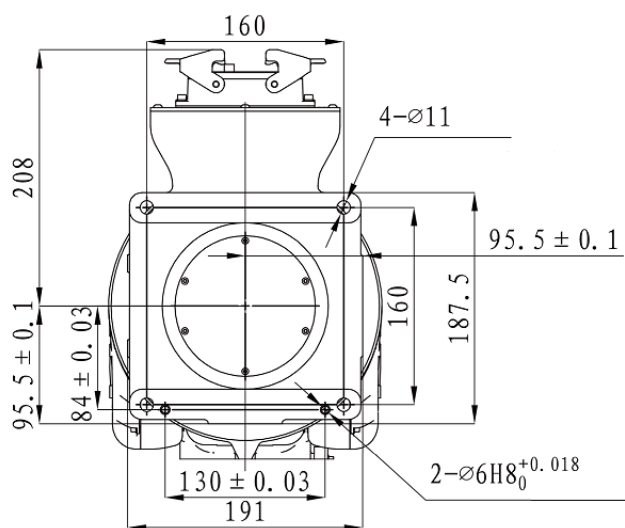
Габаритные чертежи робота-манипулятора SD7-700.
